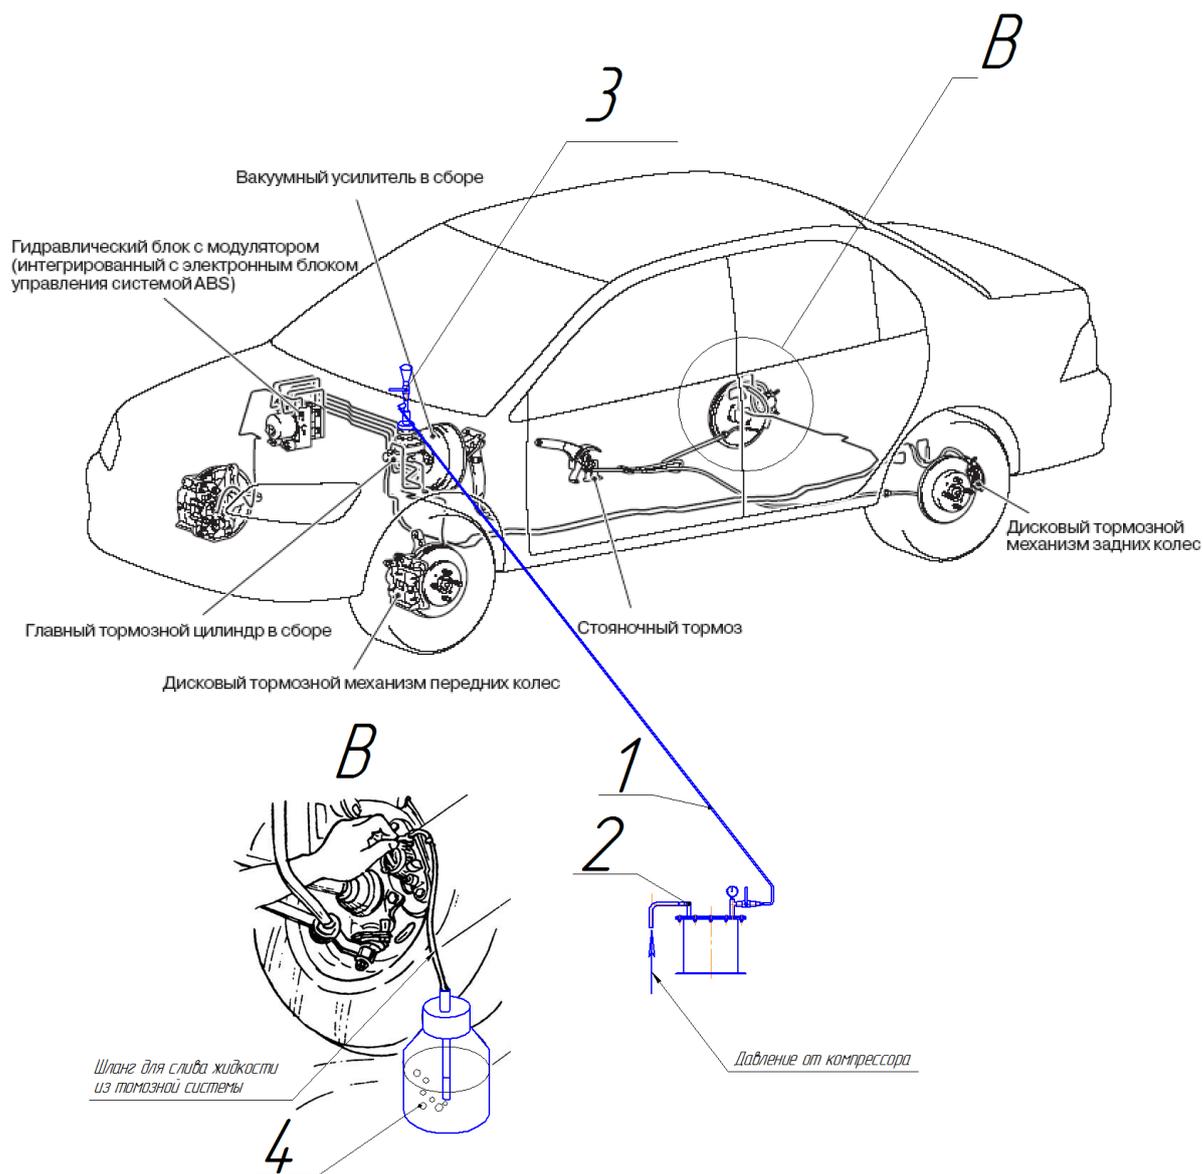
Схема установки по прокачки гидравлической тормозной системы автомобиля
